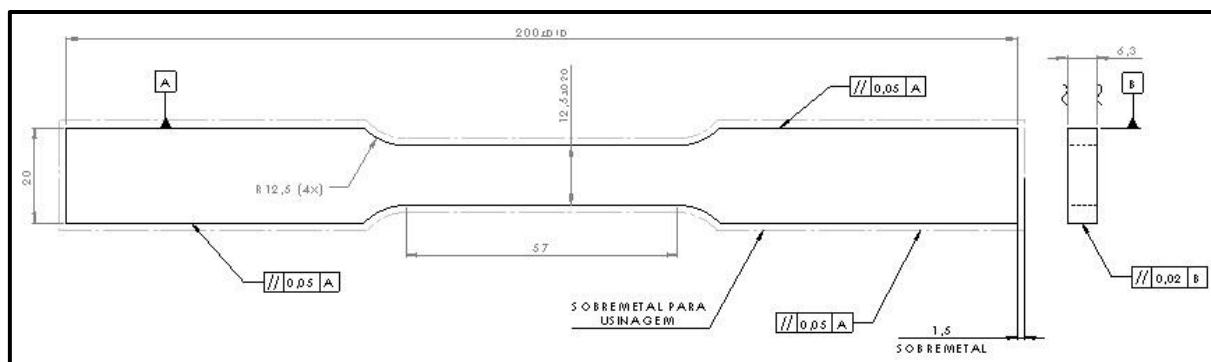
Geometria dos corpos de prova para ensaio de tração.
